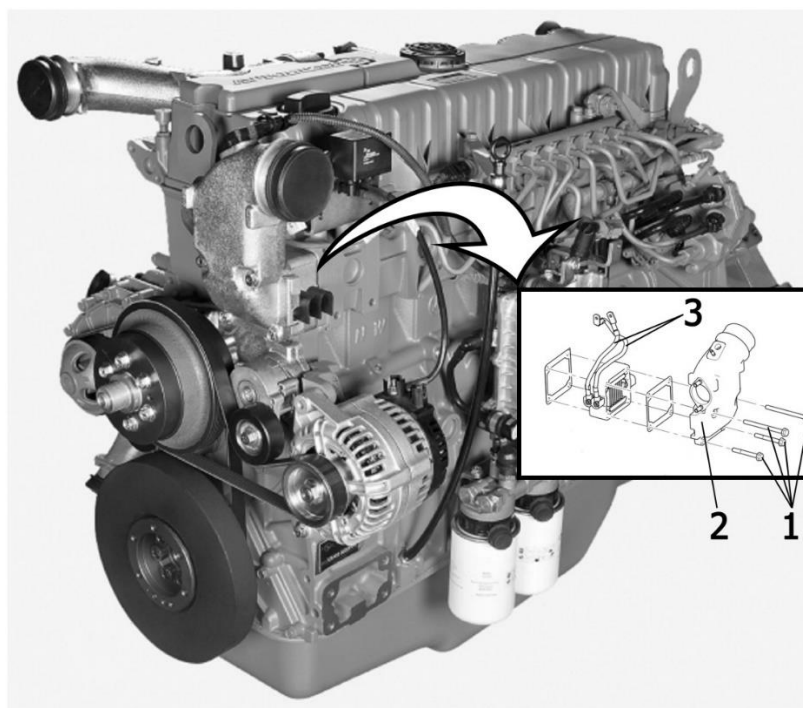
Теплоэлемент подогрева воздуха для облегчения пуска двигателя
